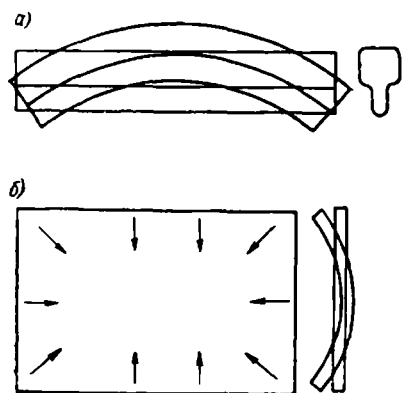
Схемы коробления отливок (в процессе охлаждения)
